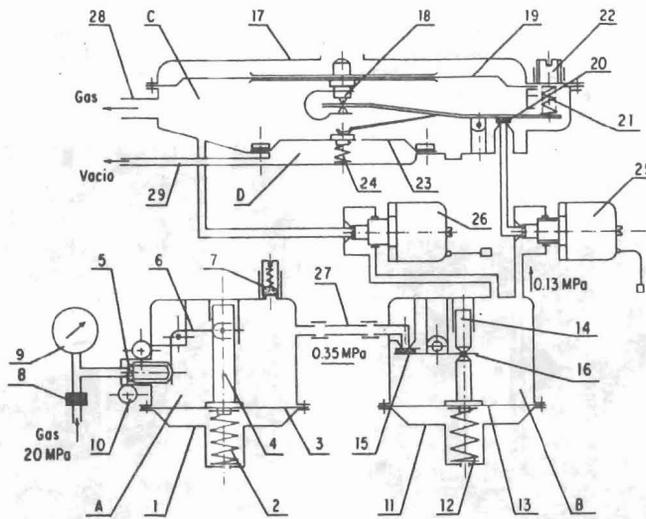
Esquema de un conjunto de reductores desarrollado en LUZ.
